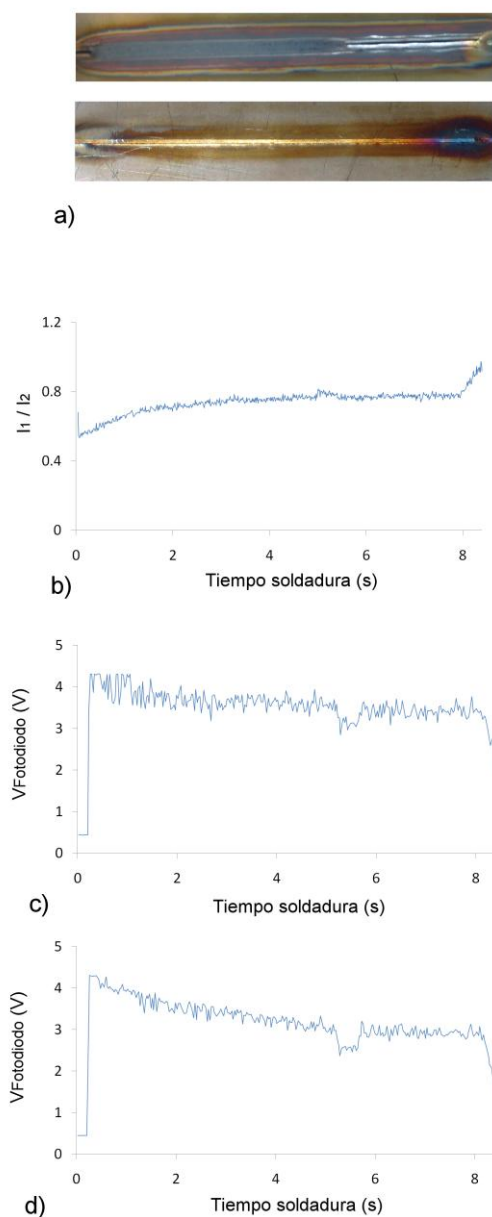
Soldadura defectuosa (variación en la corriente de soldadura).
